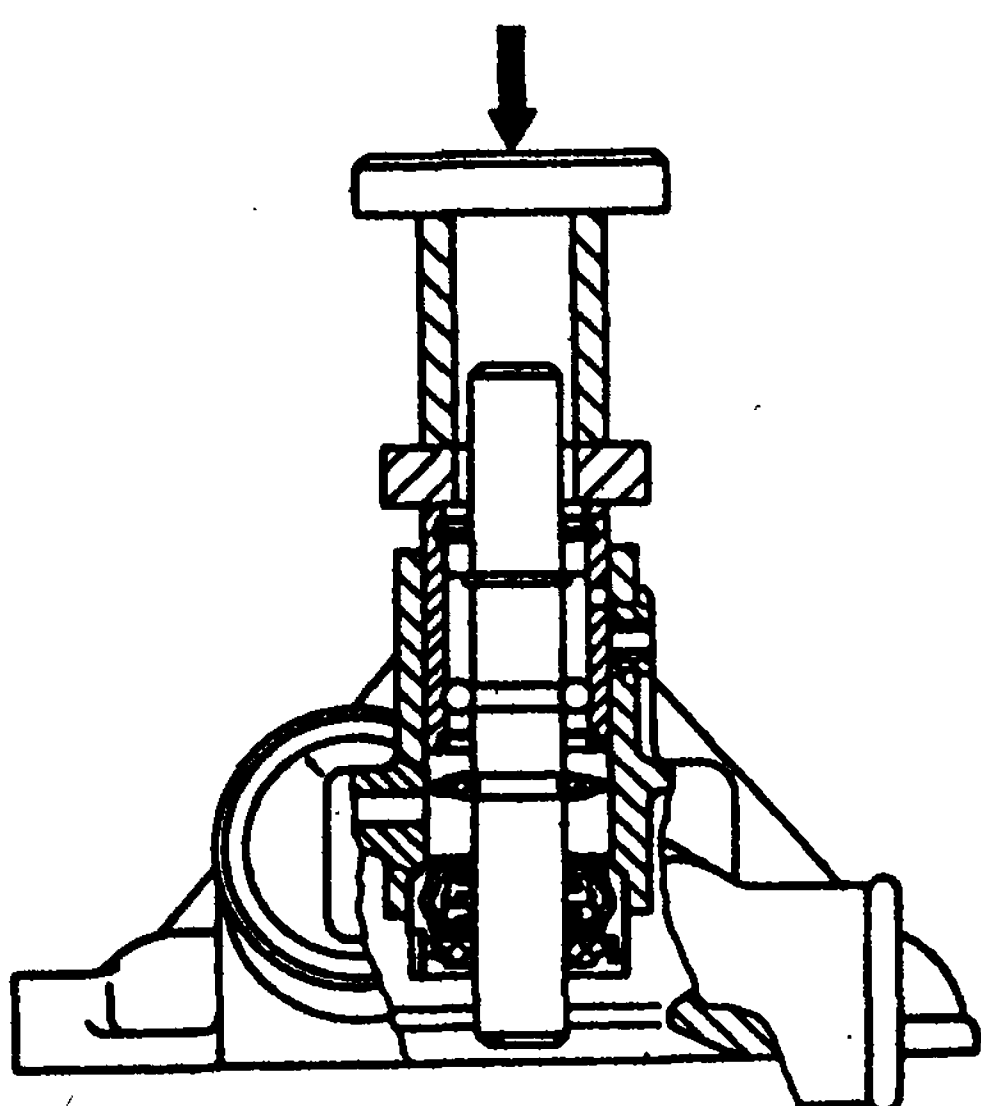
Запрессовка подшипника с валом водяного насоса
